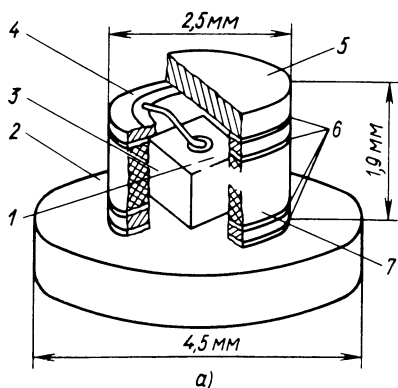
Лавинно-пролетный диод в металлокерамическом корпусе:
